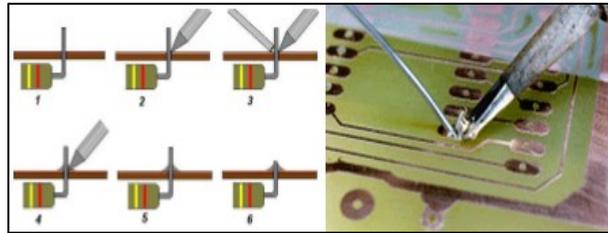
Procedimiento de soldado de elementos en circuitos impresos.
